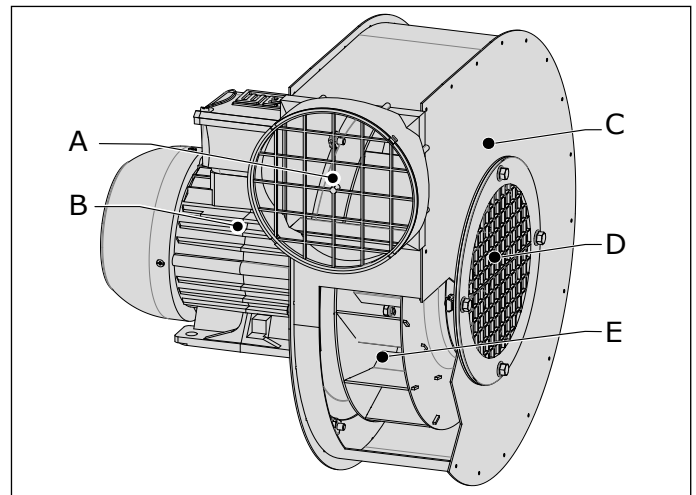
Hauptkomponenten FUA-1800/2100
